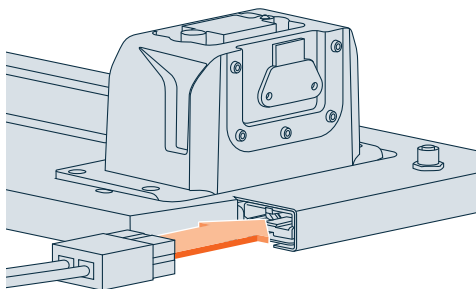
Branchement du câble d'alimentation sur le betterLink.
